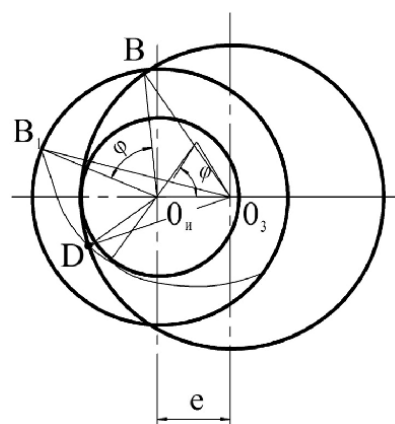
Схема скоростного фрезерования резьбы при внутреннем касании инструментальной головки с обрабатываемой поверхностью заготовки
